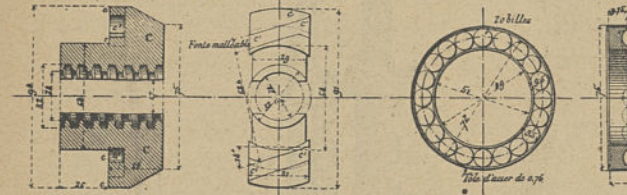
Coupe et vue en bout des coussinets. Fig 5
